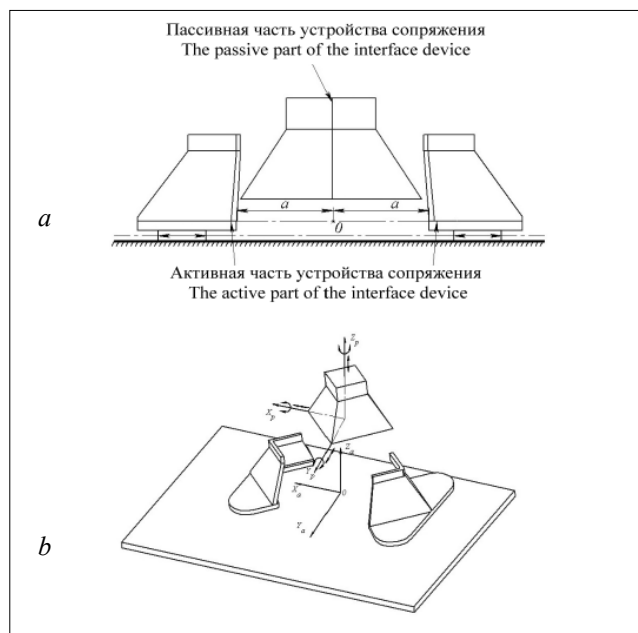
Устройство сопряжения: а – конструктивно-кинематическая схема; б – привязка систем отсчета к пассивной и активной части
